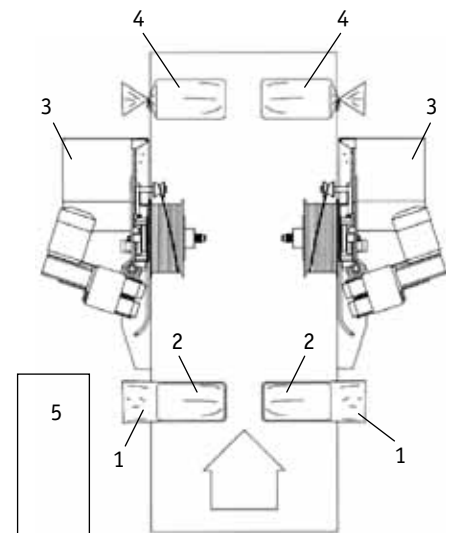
Схема установки для упаковывания хлеба в готовые пленочные пакеты типа Gusset bag with flat botton: 1 — загрузочное устройство; 2 — пакуемый хлеб; 3 — узел клипсования; 4 — упакованная продукция; 5 — пульт управления
